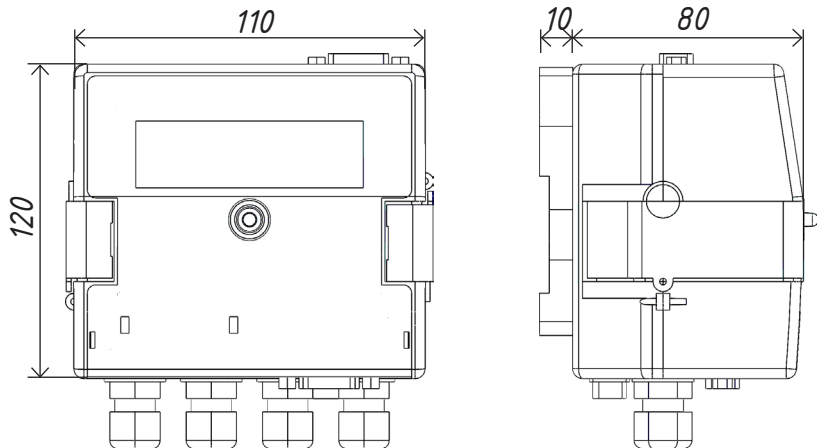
ж - Габаритные размеры электронного блока с накладкой для крепления на DIN – рейку
